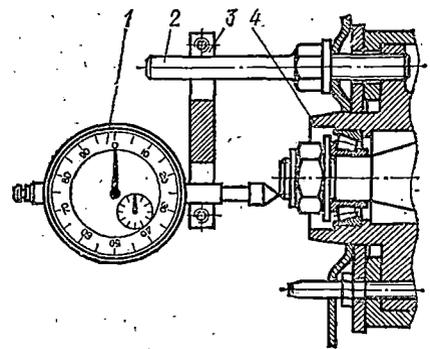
Приспособление 02.7834-9505 для измерения зазоров в подшипниках ступицы переднего колеса:
